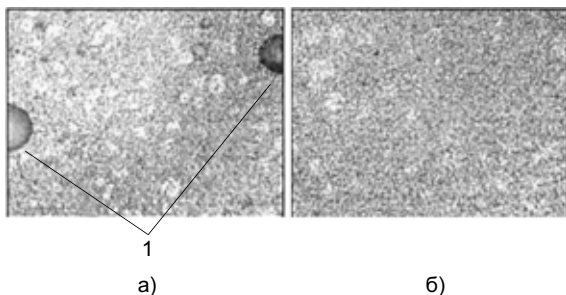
Микрошлифы швов, полученных при сварке током 140—160 А обычным полуавтоматом (а) и с импульсной подачей проволоки (б): 1 — включения в сварном шве
